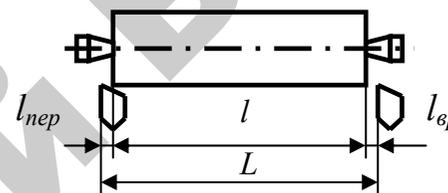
Длина обработки (рабочего хода инструмента)
